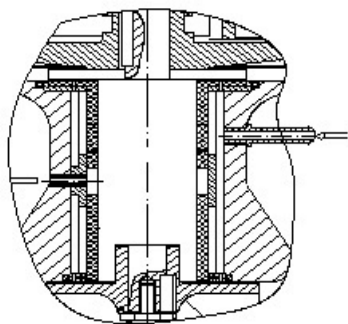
Конструкция ротора турбокомпрессора на воздушной смазке
